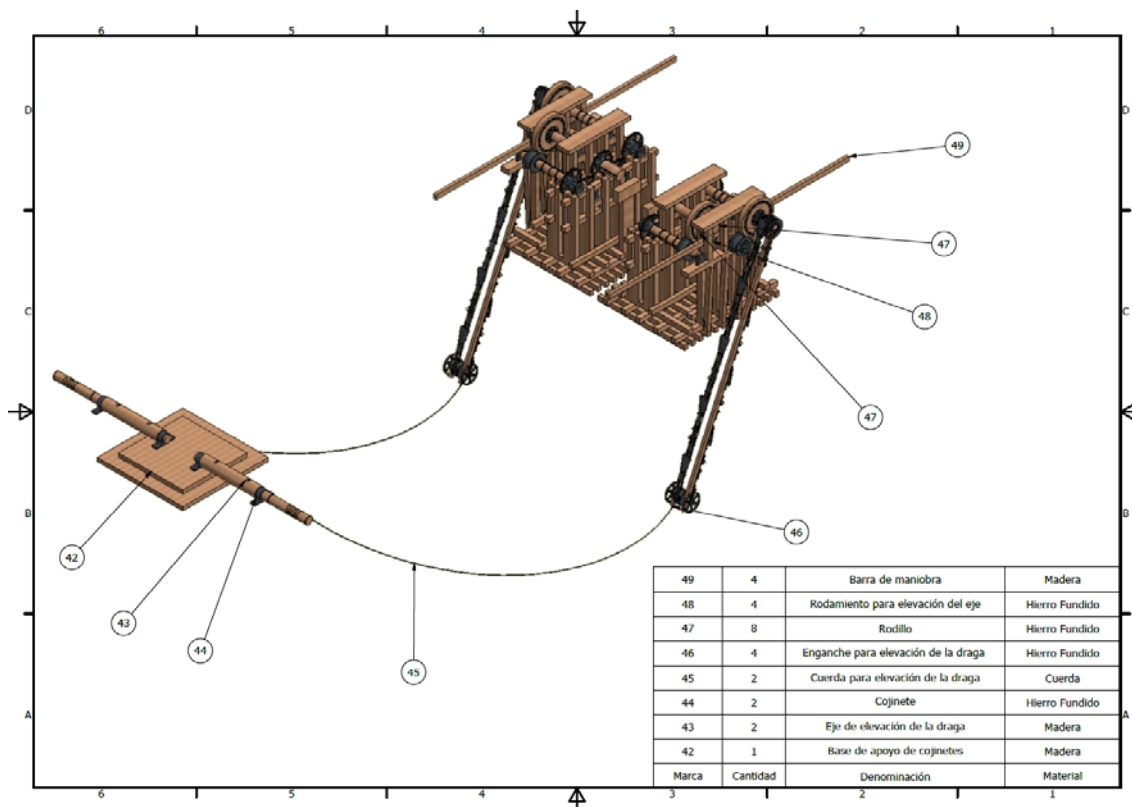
Plano de conjunto del sistema de maniobra y elevación de la draga.
